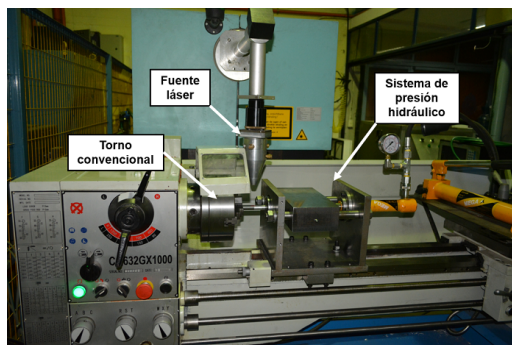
Equipo de soldadura por fricción con asistencia láser (LAFW)
